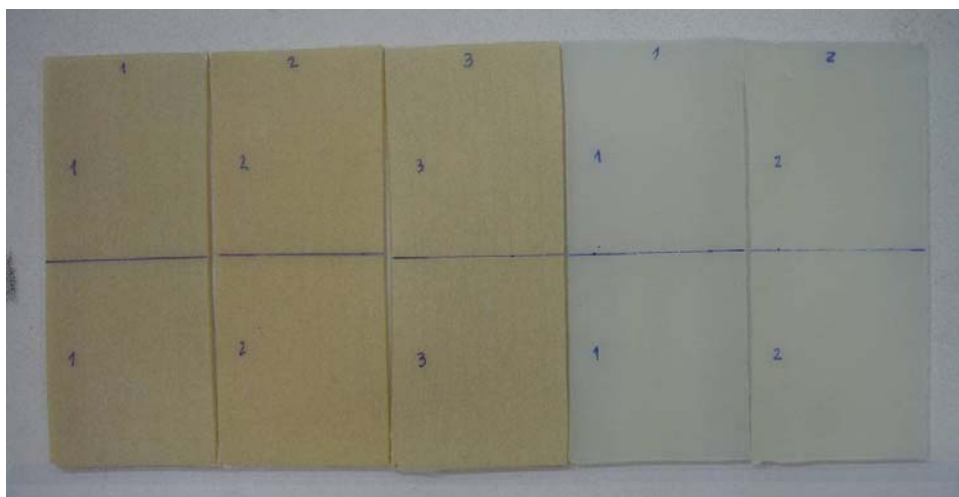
Diversas placas de adesivo para fabricar provetes Arcan.
